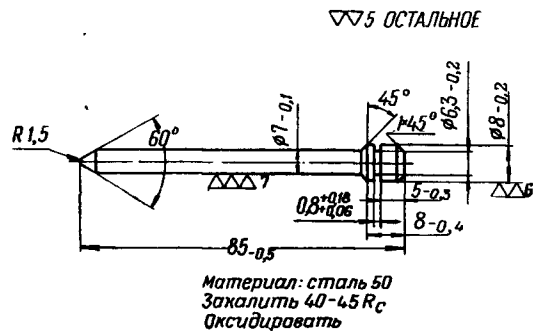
Палец ударника (3-21) пулемета последних годов изготовления
